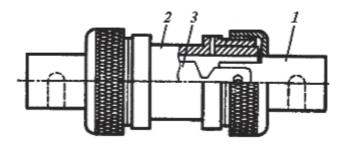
Плавкий предохранитель типа ПР: 1- контактный нож; 2- патрон; 3- плавкая вставка
